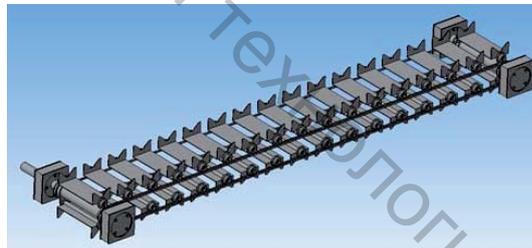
Схематический вид транспортера для перемещения стального патрубка
